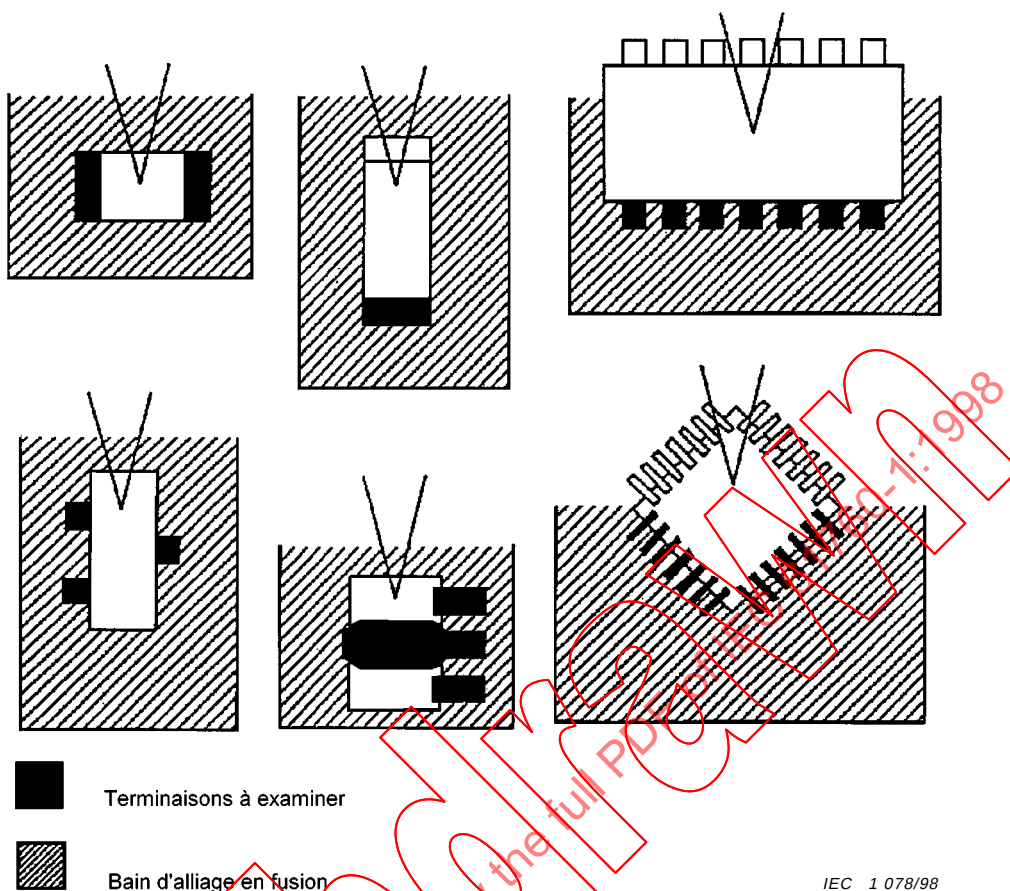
Exemples d'immersion pour l'essai de brasabilité
